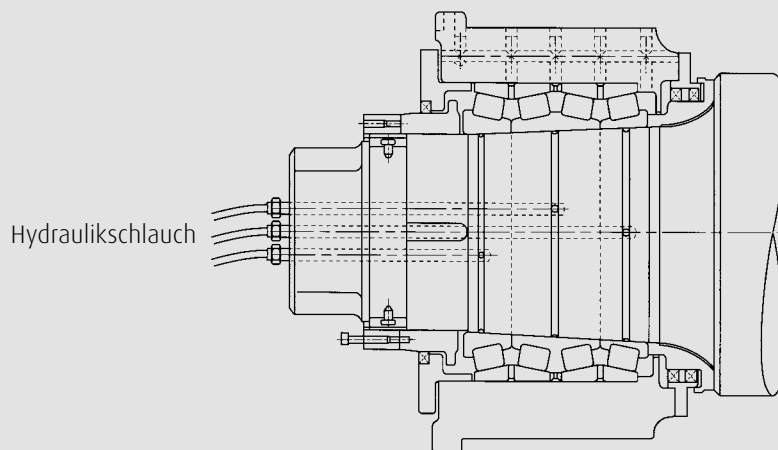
Ausbau des Lagers mit Festsitz auf kegeligem Sitz mit dem Öldruckverfahren
